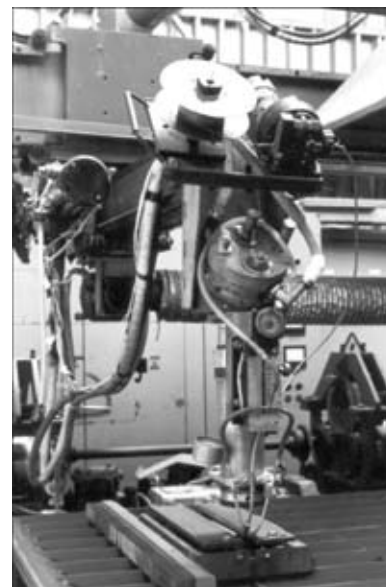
Общий вид фрагмента двухкоординатного манипулятора со сварочной головкой и механизмом подачи присадочной проволоки
